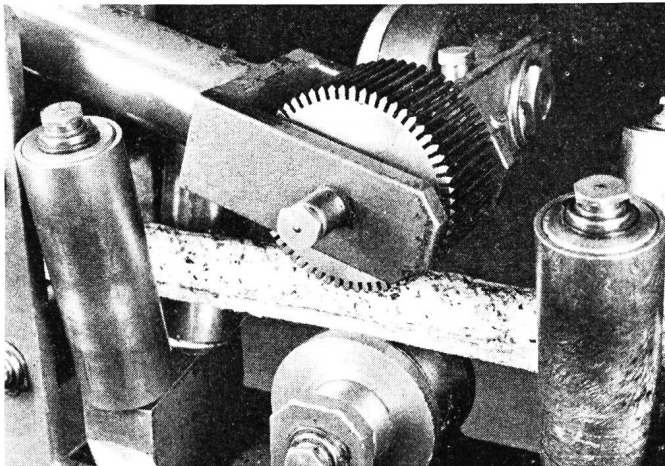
Gezahntes Messrad. Die vom Kabel abfallende Teermasse und die Kalkmilch können durch die Zahnluken fliehen, deshalb bleibt die Abrolllänge immer genau 250 mm. Laufrichtung des Kabels von rechts nach links
